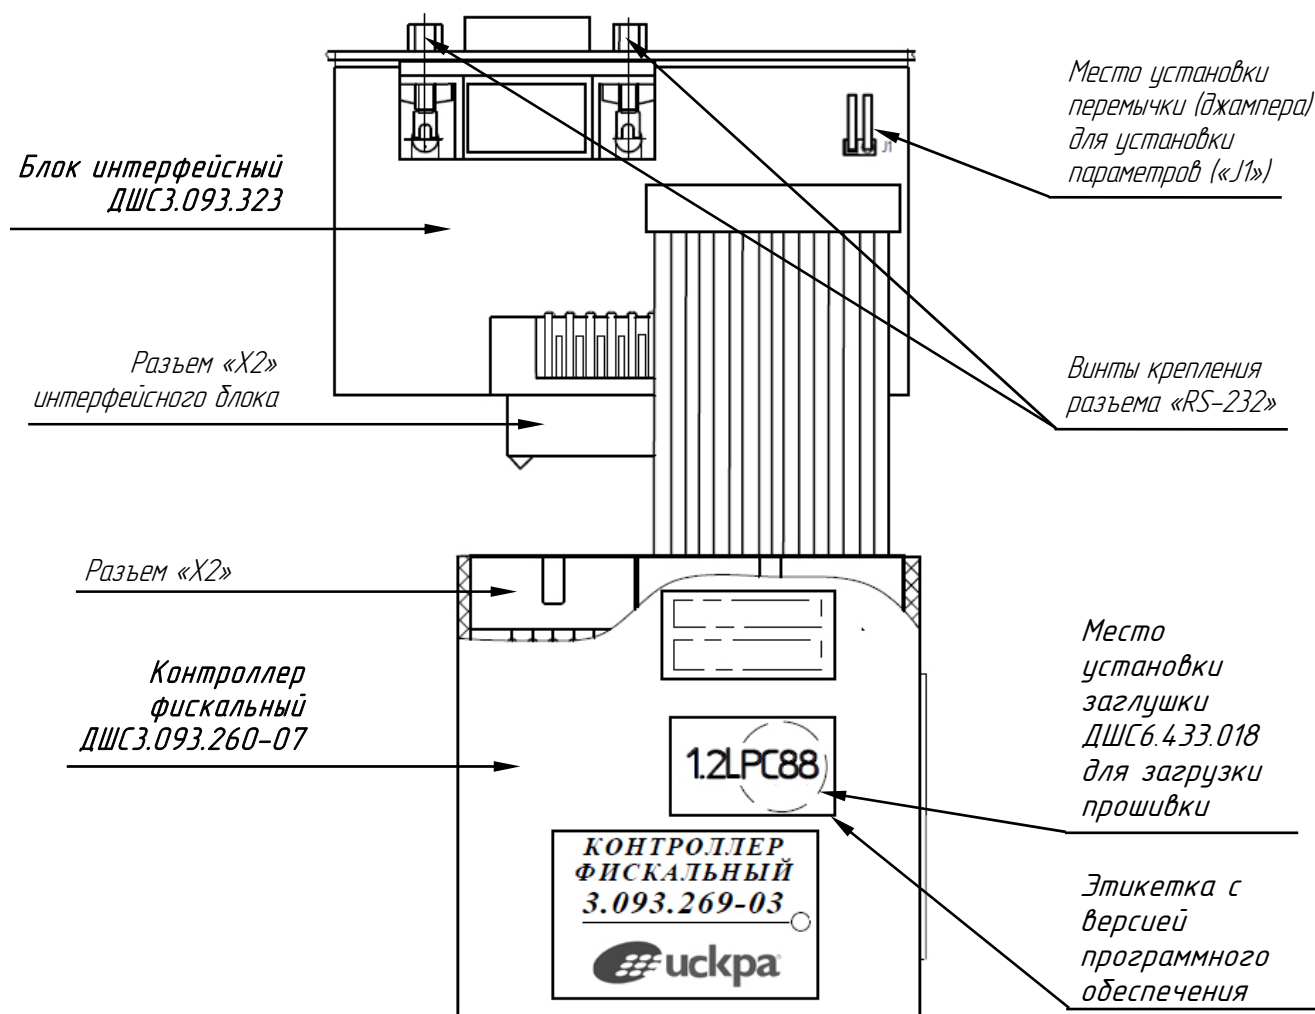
Вид контроллера фискального ДШС3.093.269-03
